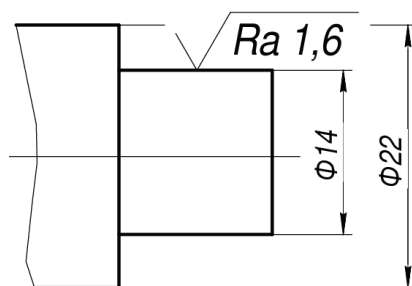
Нанесение шероховатости поверхности с разрывом выносной линии
